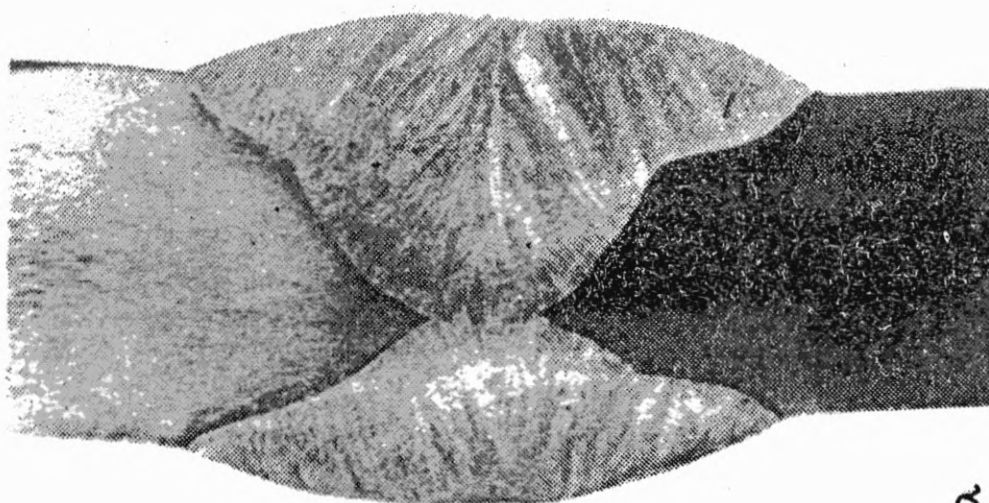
Сварка в два прохода стыкового соединения:
